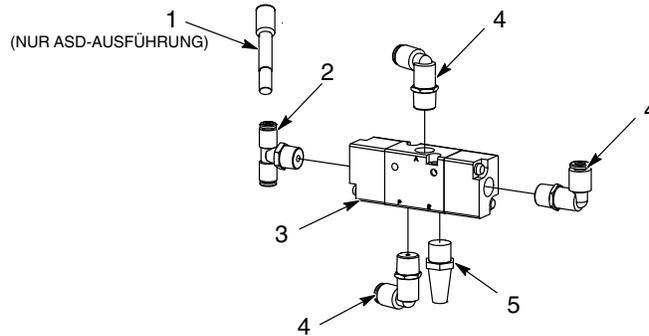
Steuerventilsatz für unregelmäßigen Druckluftmotor
